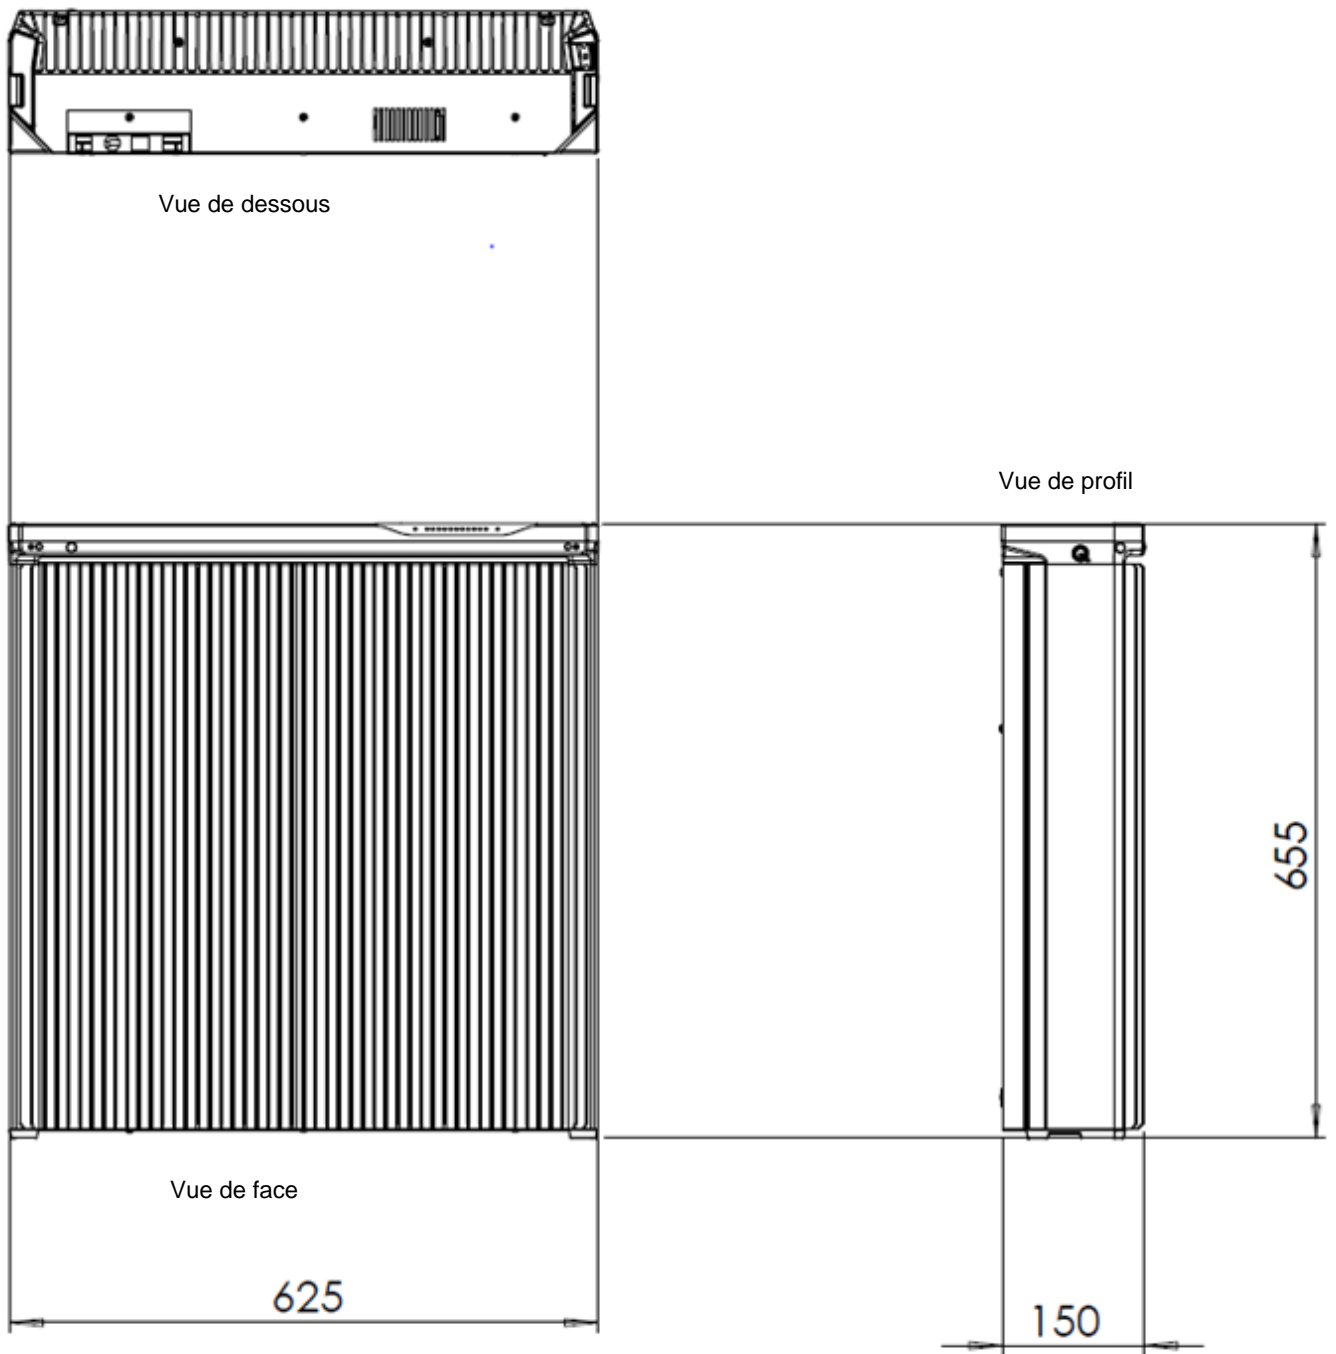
Vue avec dimensions de dessous, de face et de profil du procédé
